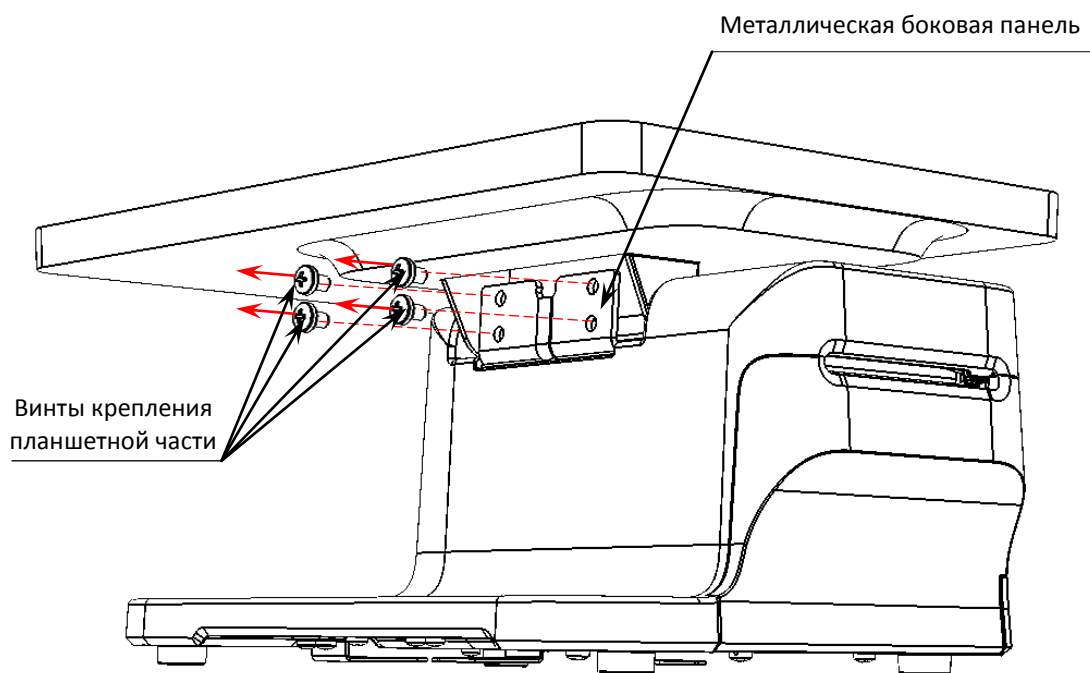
Винты крепления планшетной части к основному корпусу ККТ
